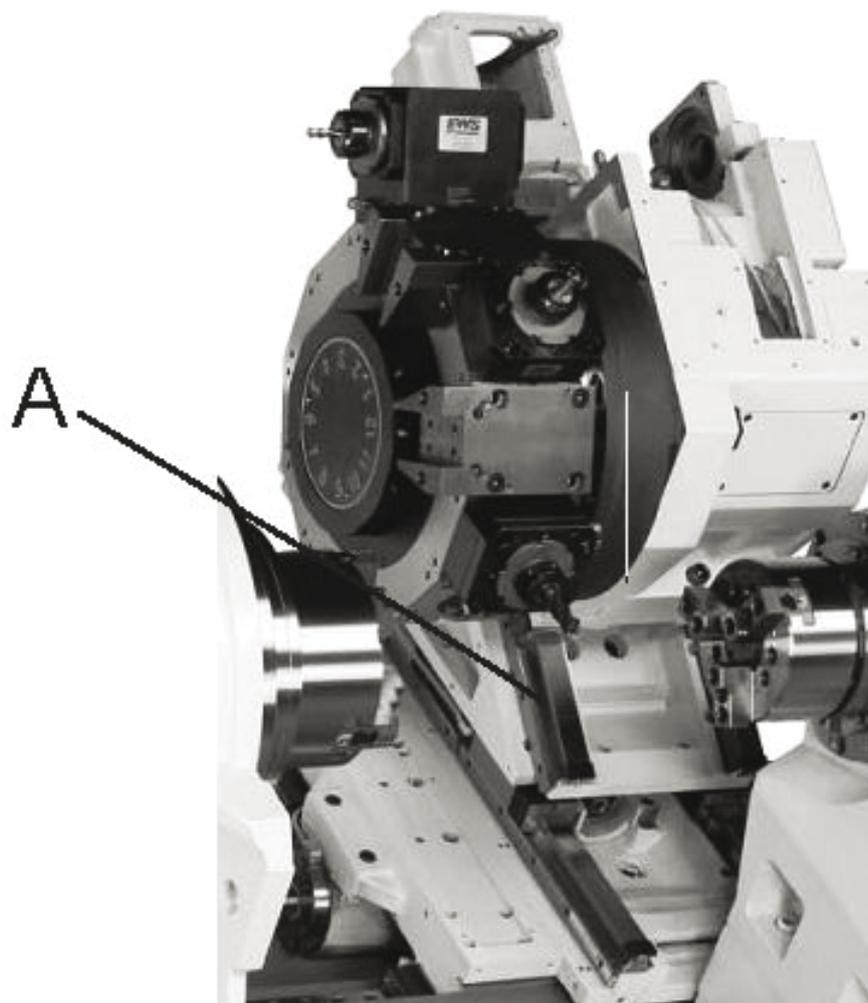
Автоматическая инструментальная головка токарного станка модели FNL-320SY
